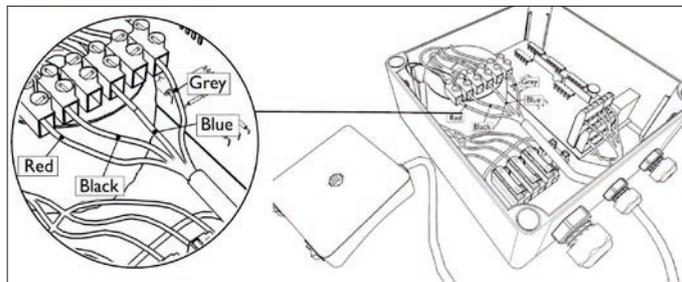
S-100, SK-300 & Haubenbeleuchtung
